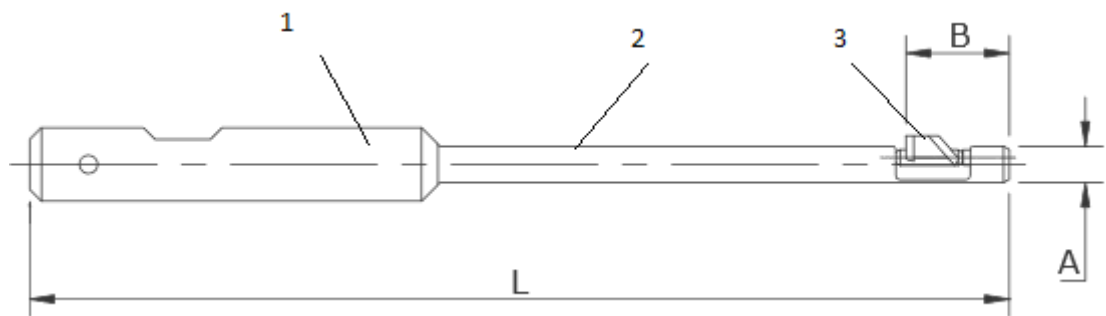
Розточна головка фірми Cogsdill моделі Flipcut[2]
